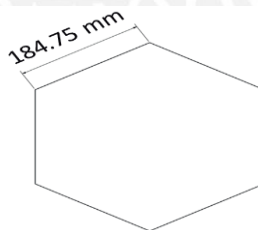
Vista frontal de la tapa del tambor. Fuente: Propia
